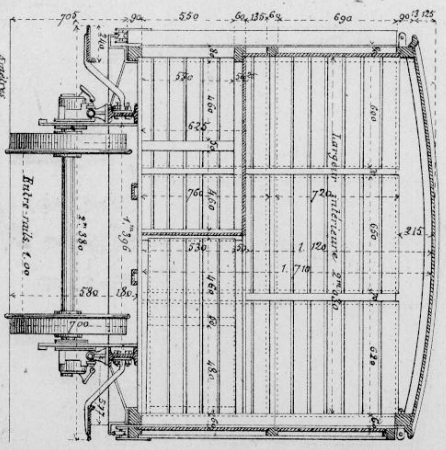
Elevation, Coupe transversale à 0^m03 pour 1^{er} Mètre.
